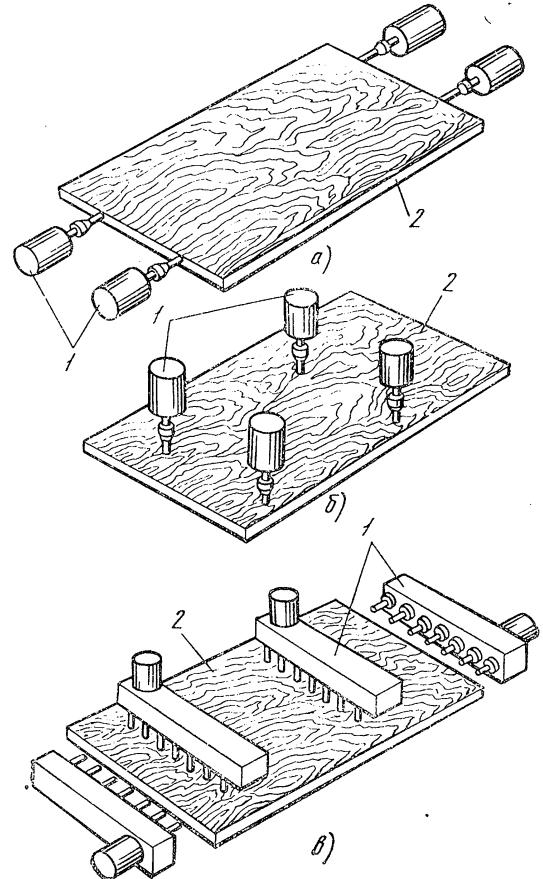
Схемы сверления круглых отверстий на сверлильно-присадочных станках:
